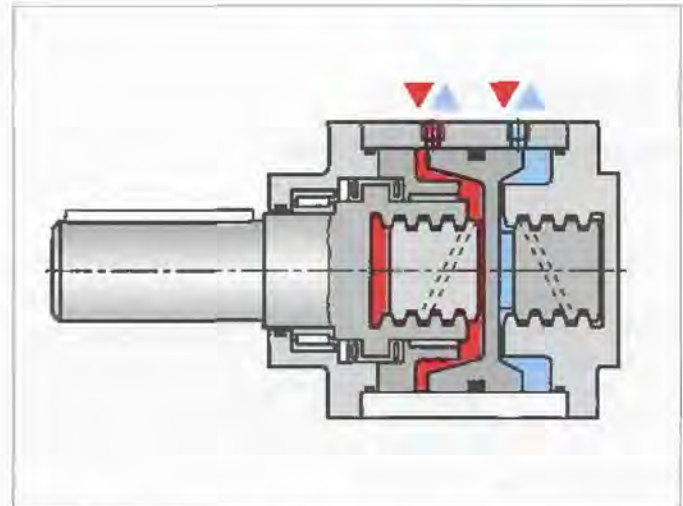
Поворотный гидродвигатель, приводимый в движение с помощью разнонаправленной резьбы
